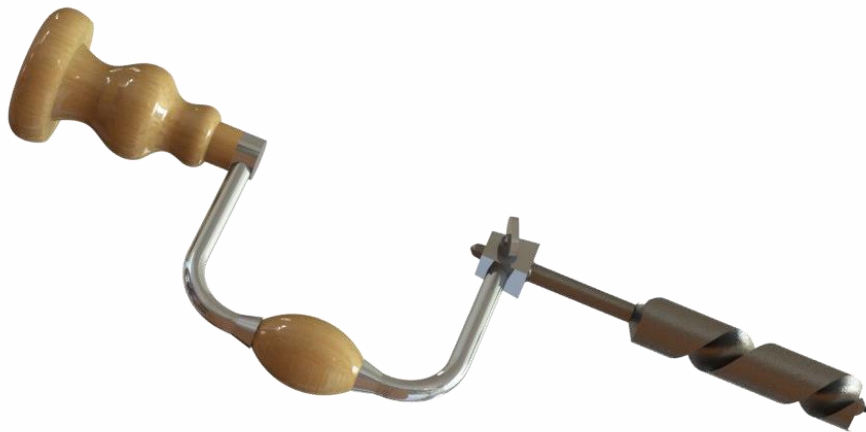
alter Kurbelbohrer oder Brustbohrer mit Holzgriffen
